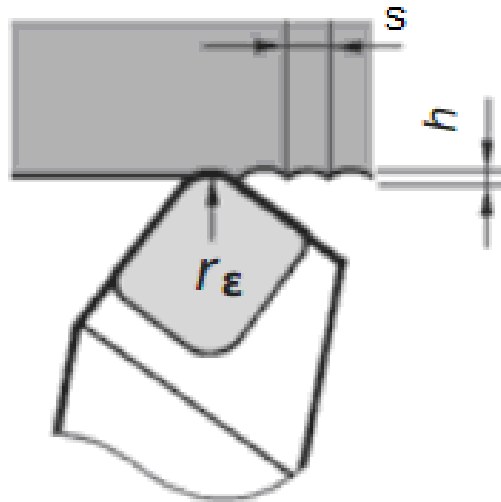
Схема образования шероховатости поверхности при точении [4]
